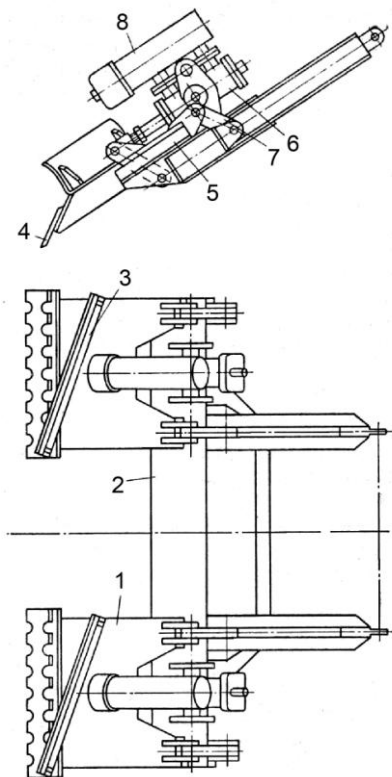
Схема скальвателя с пассивным рабочим органом:
